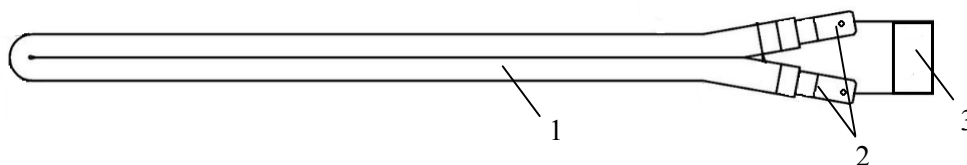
Ленточный подогреватель в развернутом виде: 1 – ленточный кольцевой электронагревательный элемент; 2 – контактные зажимы; 3 – блок управления.
